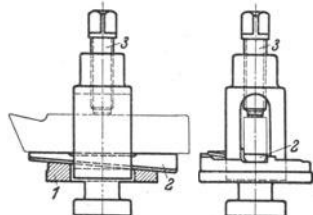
Stahlhalter mit Höheneinstellung (Loewe, Berlin).
